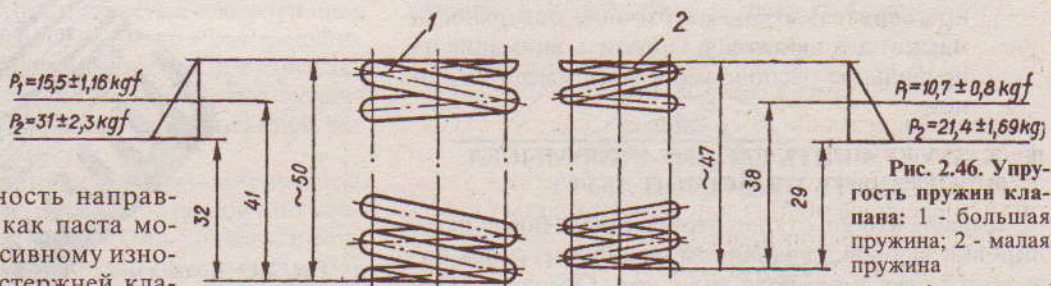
Упругость пружин клапана: 1 - большая пружина; 2 - малая пружина
